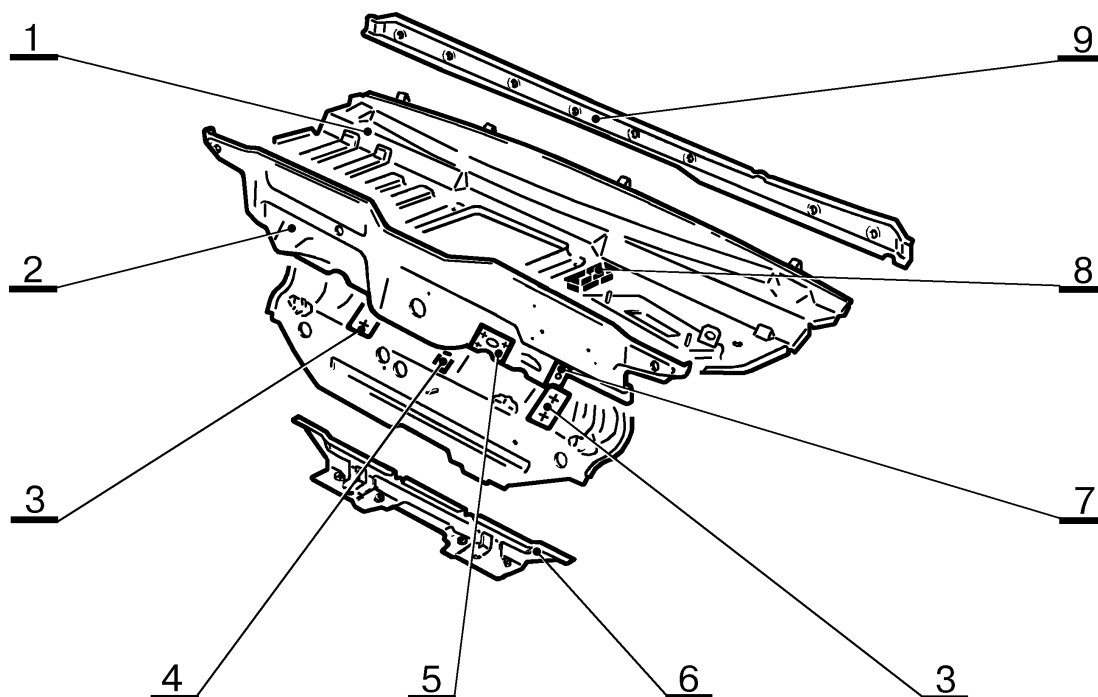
Детали щитка 2108-5301080 передка в сборе. Номера и наименования деталей, количество сварочных точек приведены в таблице 11.
